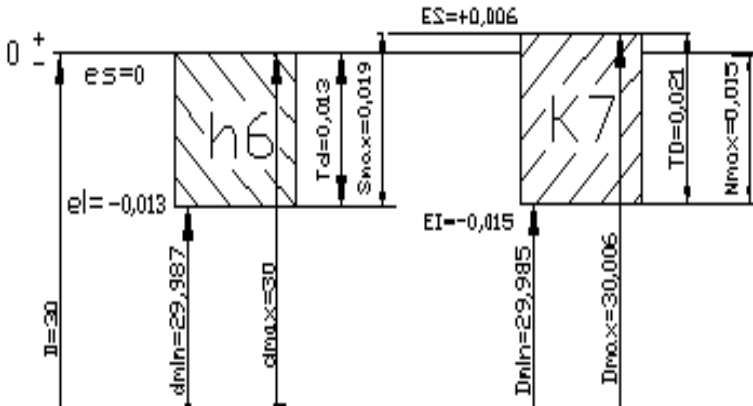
Схема розташування полів допусків отвору і вала посадки $\varnothing 30 \frac{K7}{h6}$
